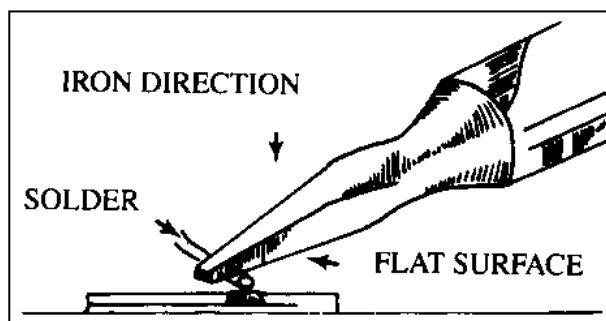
Colocación del cautín y la soldadura.
